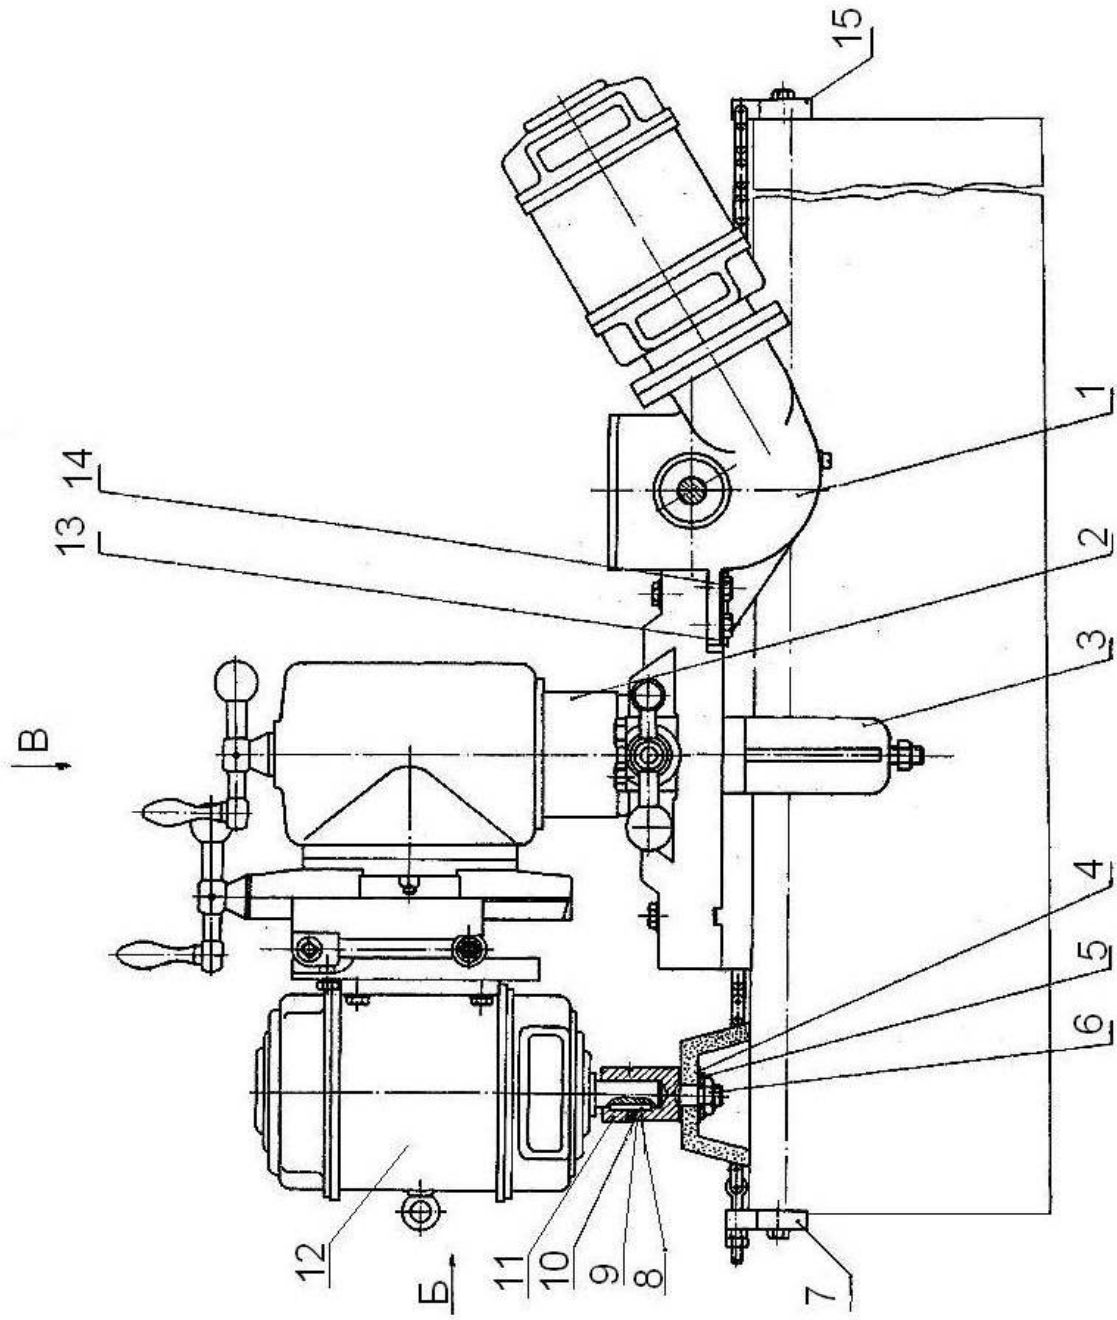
Приспособление для шлифования направляющих токарных станков СД 7191 – 4001
